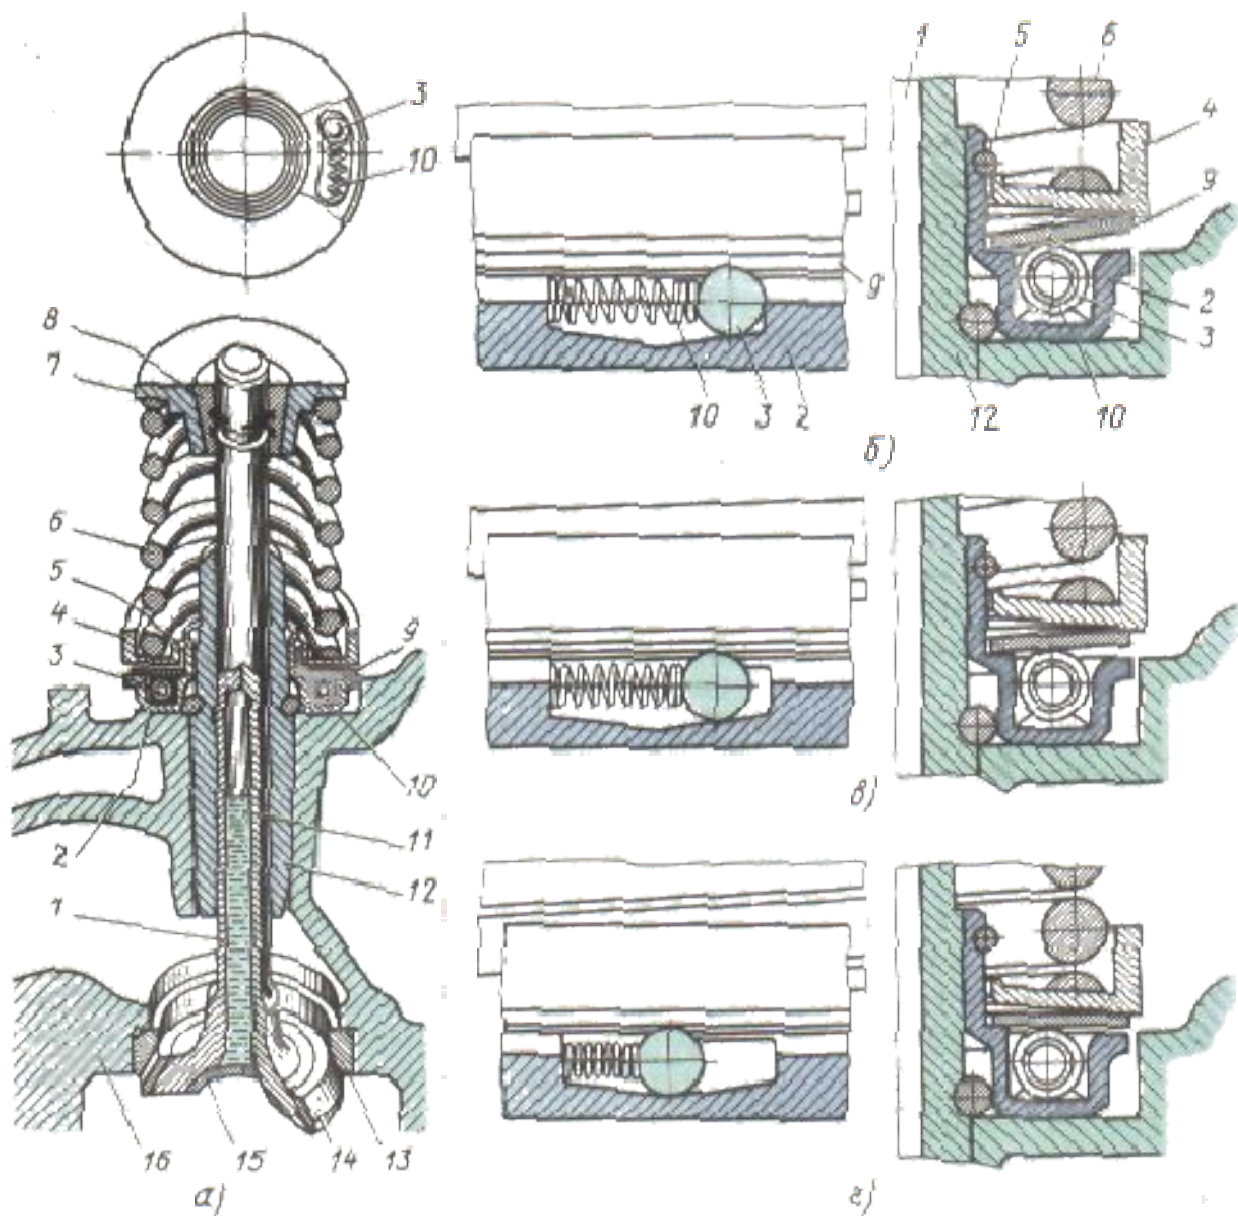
Выпускной клапан двигателя автомобиля ЗИЛ-130 с механизмом вращения
